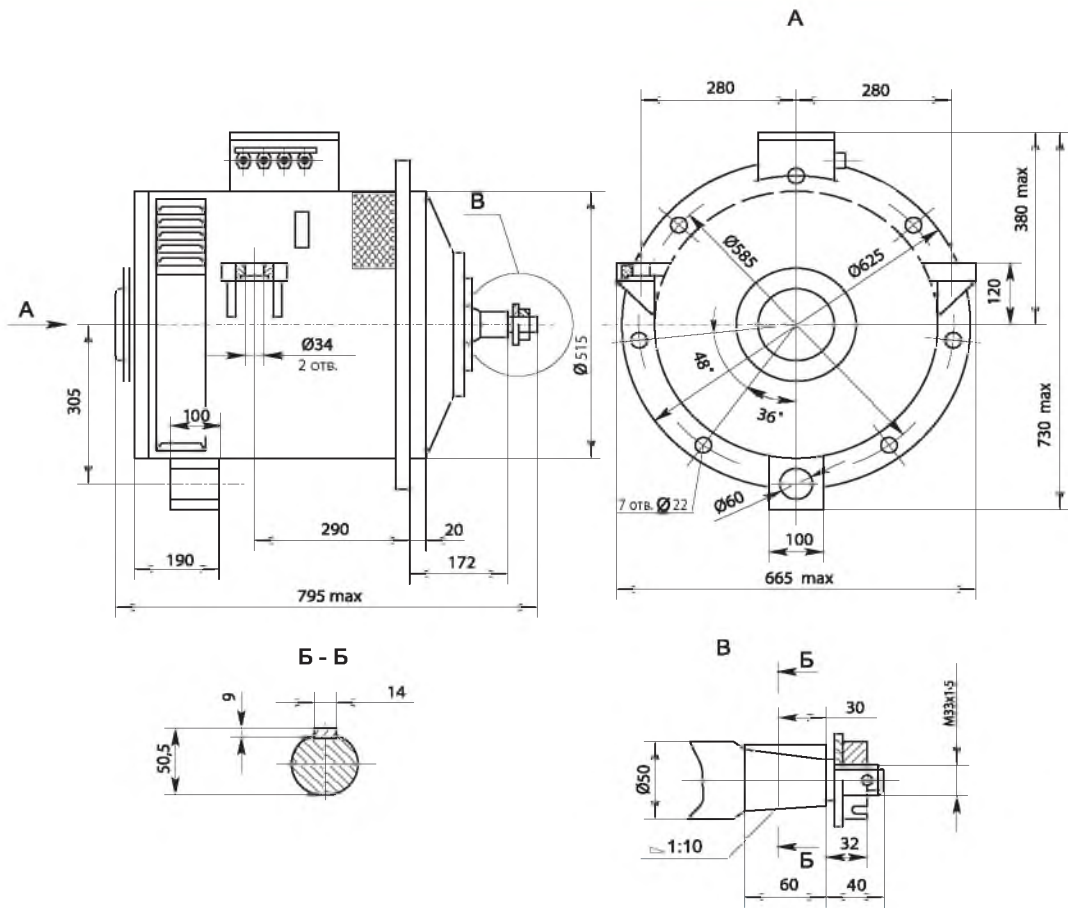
Габаритные и установочные размеры электродвигателя ДТН-46/33М
